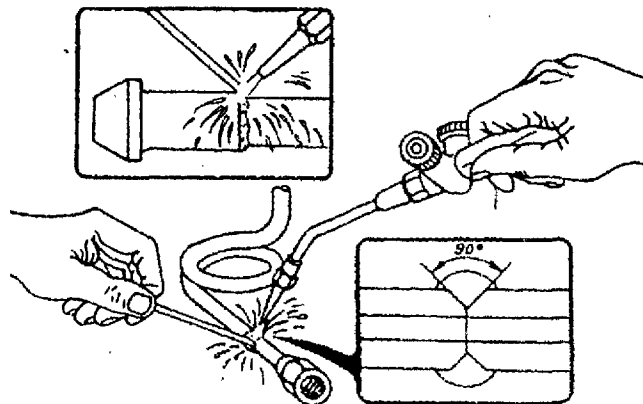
Приварка наконечника и сварка изломанного трубопровода
